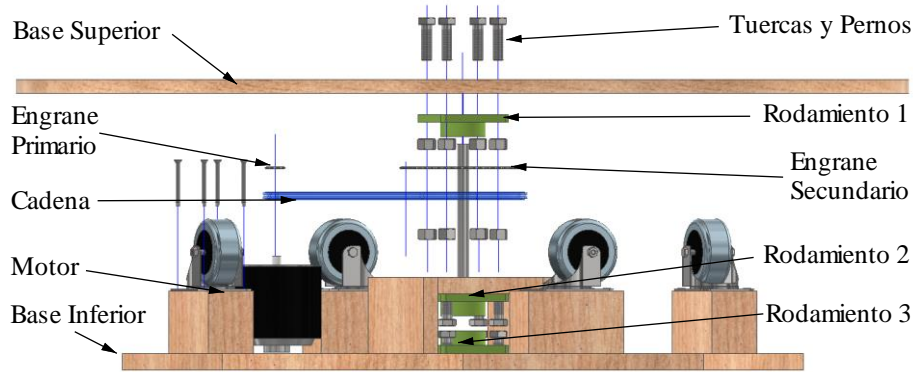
Vista explosionada de base giratoria. (Fuente propia).
